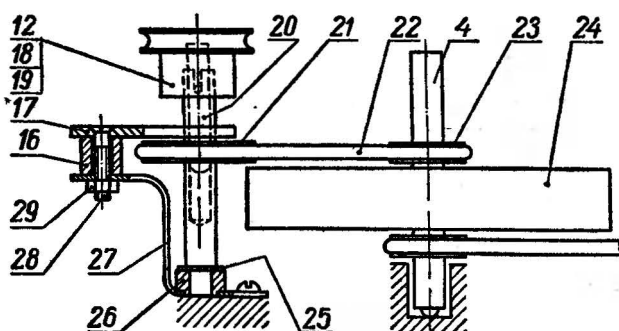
Механизм привода дополнительного приемного узла: 4 — ведущий вал; 12 — шкив; 16 — стойка, высота по месту, Д16-Т, 2 шт.; 17 — планка, Ст.20; 18 — штифт; 19 — направляющая; 20 — полый вал; 21 — шкив большой; 22 — пассив; 23 — шкив малый; 24 — маховик; 25 — шайба, Ст.20, лист толщиной 0,5 мм; 26 — втулка, ЛС59-1, развальцевать в кронштейне 27; 27 — кронштейн; 28 — винт М4×20, 2 шт.; 29 — гайка М4, 2 шт.
